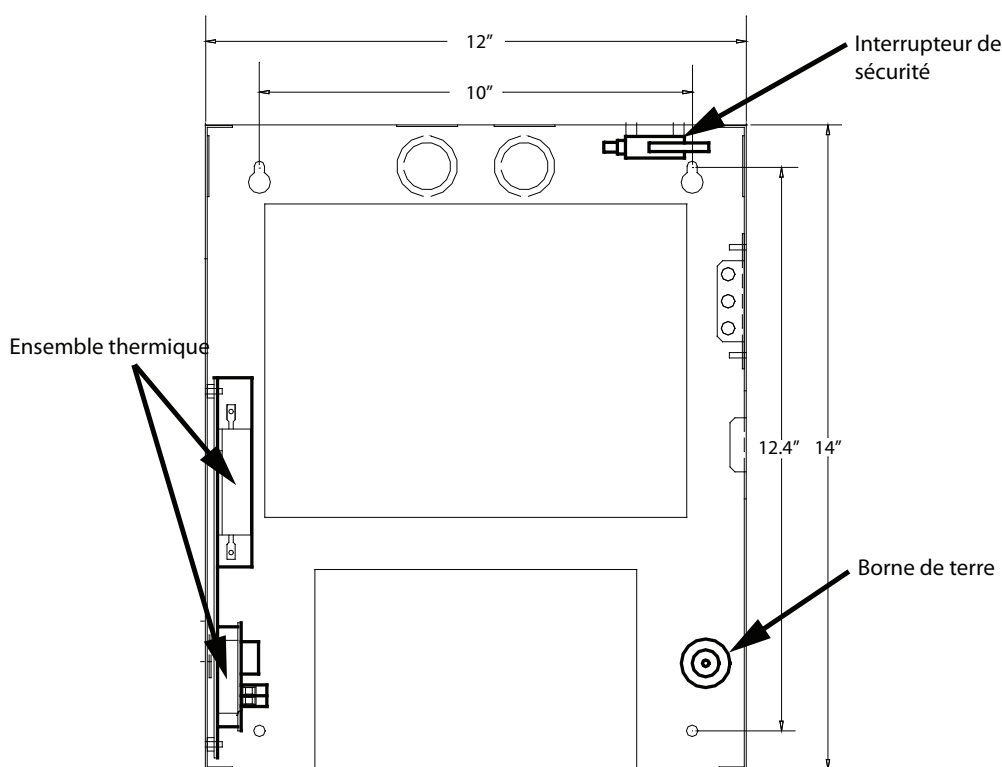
Dimensions du capotage arrière du contrôleur et l'emplacement de composant facultatif
